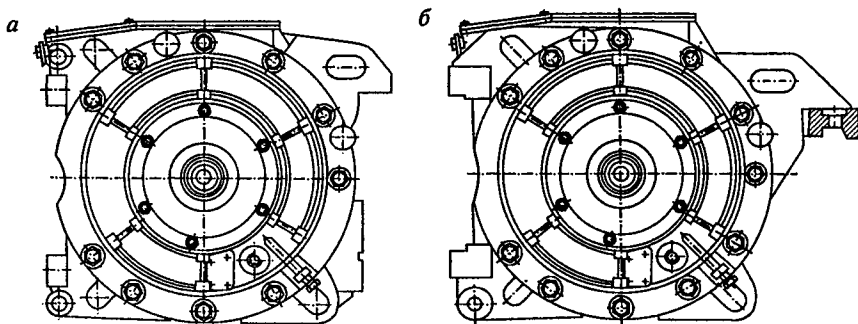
Варианты исполнения корпуса тягового электродвигателя ДАТ-510: *а* — опорно-осевое подвешивание с подшипниками качения; *б* — опорно-рамное подвешивание
